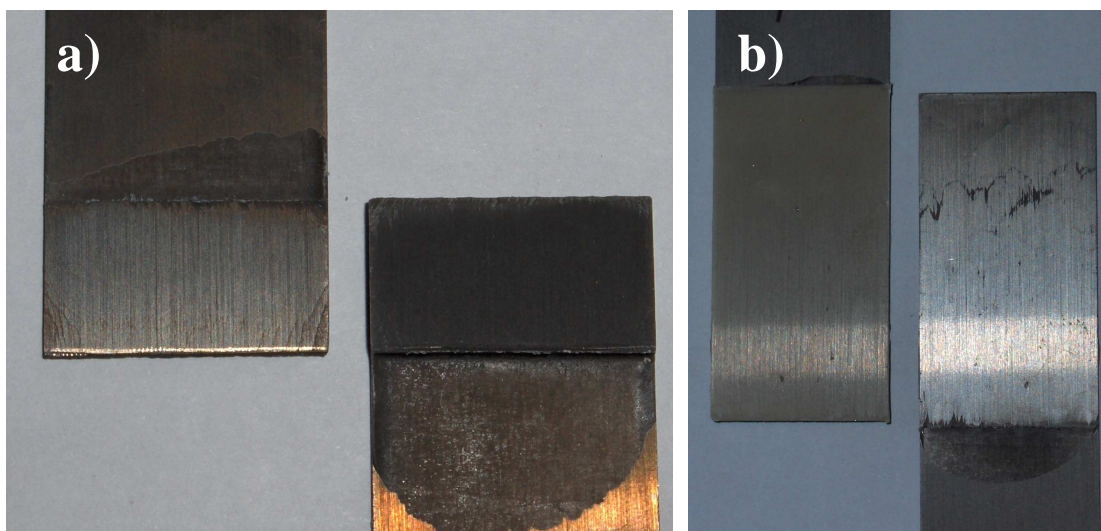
Rotura adesiva a) ensaio nº 10 e b) ensaio nº 16
